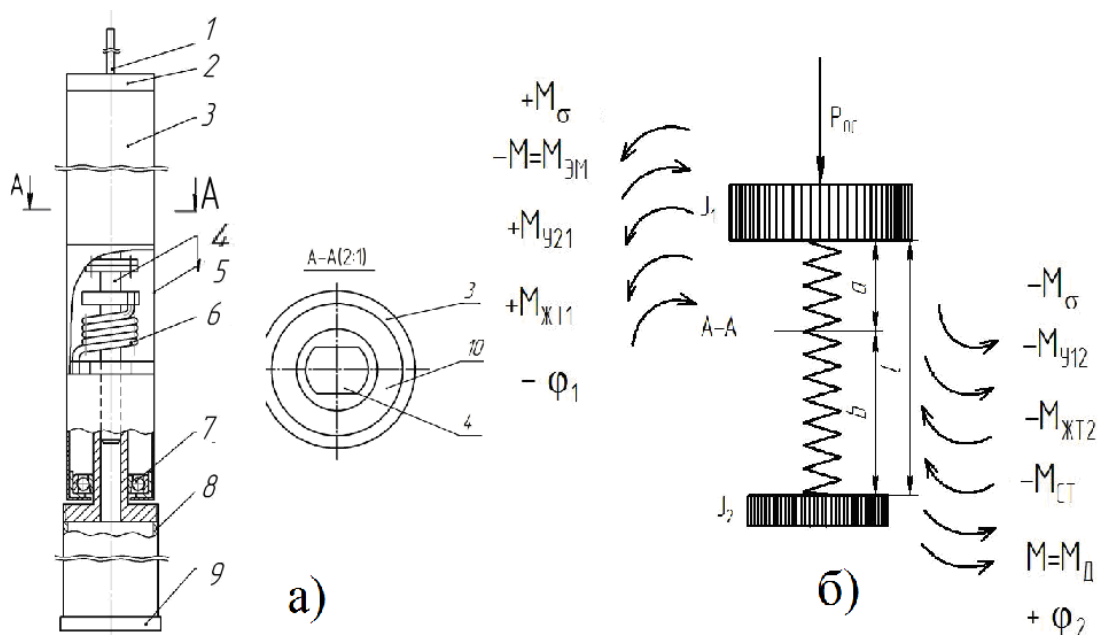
, а) Конструктивная схема ДУБС: 1-грузонесущий кабель; 2-кабельный замок; 3-ЭД с электроотсеком; 4-ротор ЭД; 5-статорная труба; 6-пружина кручения; 7-подшипниковый узел; 8-колонковая труба; 9-буровая коронка, 10-статор ЭД; б) Расчетная схема ДУБС
